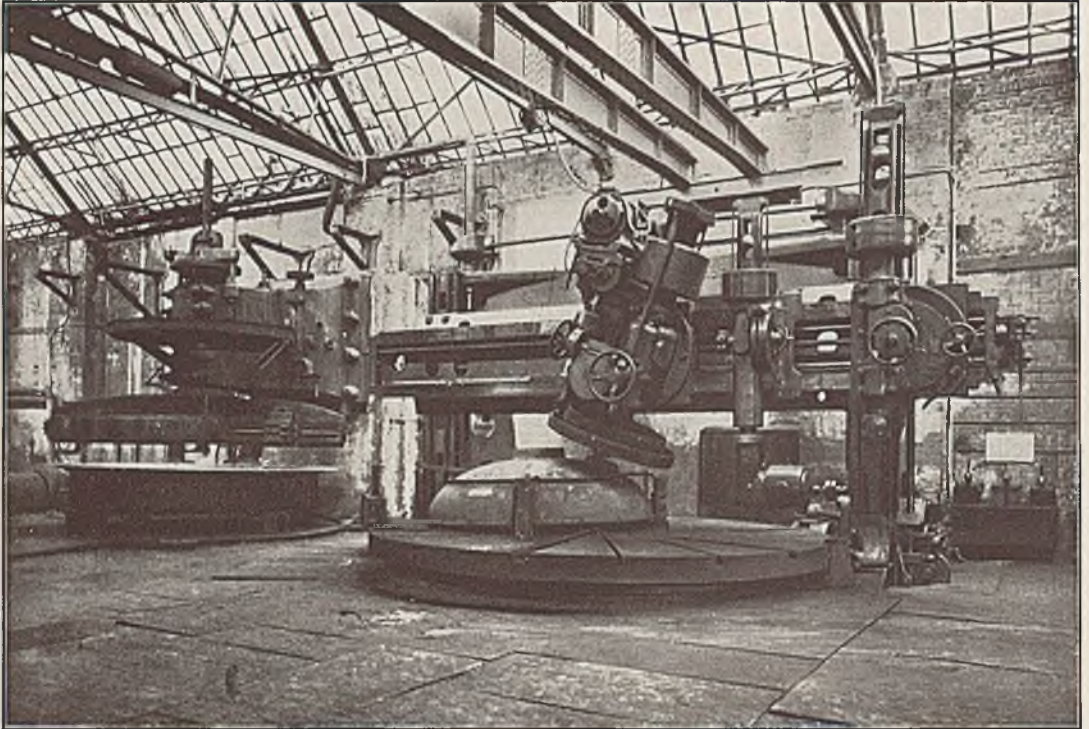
Drehbank, daneben Bodendrehbank, auf der ein aus zwei zusammengeschweißten Blechen gepresster Zellerboden von 4720 mm Durchmesser und 10 mm Stärke mit gebrochener Kante versehen wird
